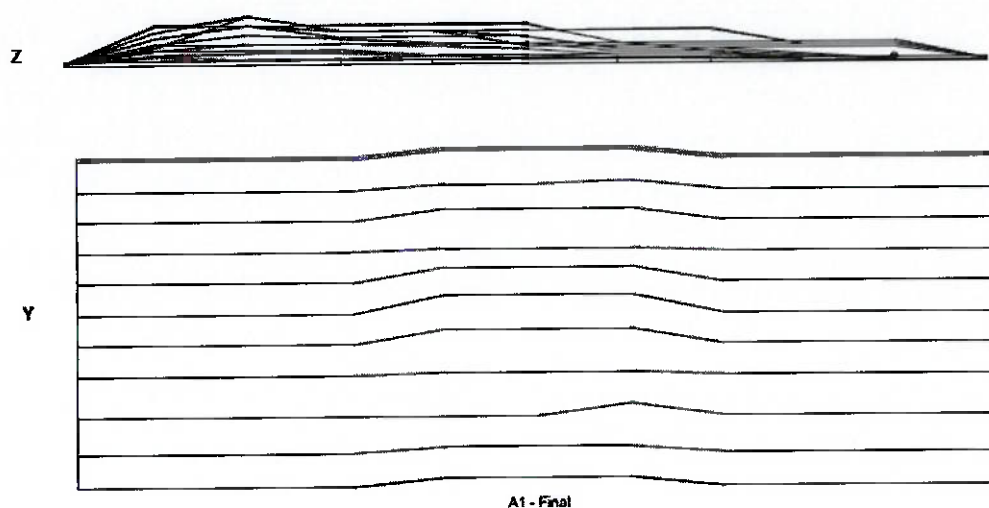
Ilustração da condição final da chapa com fator de escala após a segunda soldagem.
